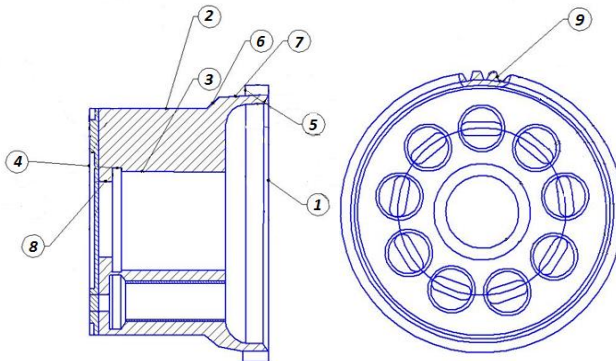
Корпусная деталь с нумерацией поверхностей: 1, 4, 5 – торцы детали, 2 и 7 – внешние цилиндрические поверхности, 3 и 8 – поверхности внутренних отверстий, 6 – конусная поверхность, 9 – канавки сложной формы
